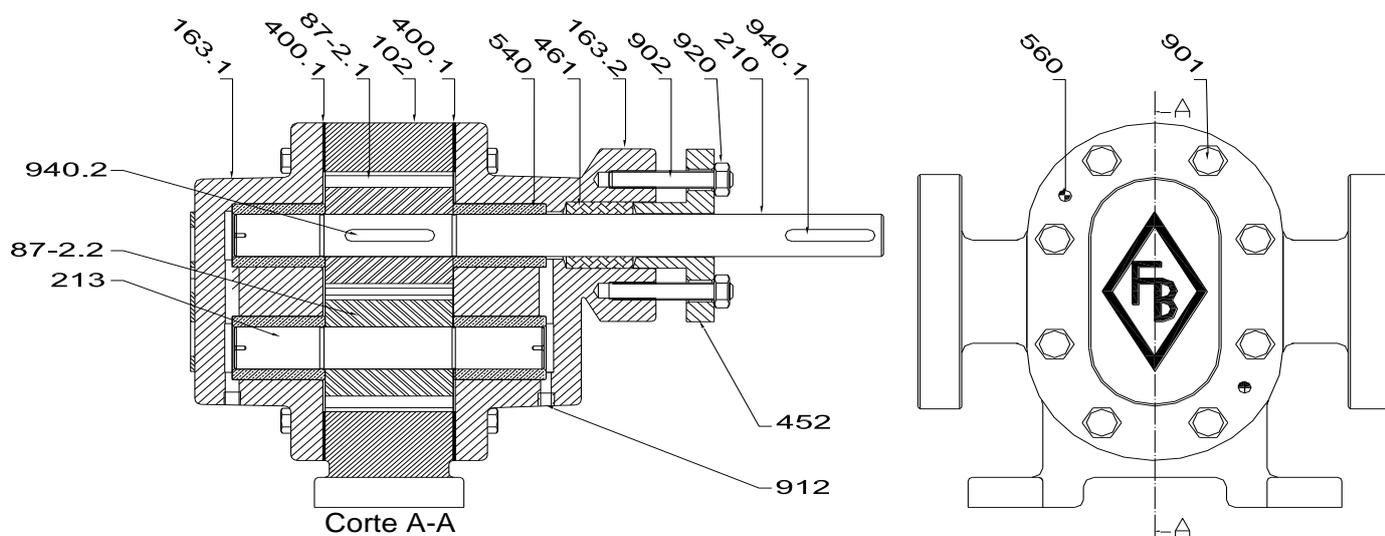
Desenho em Corte bomba FBE 1.1/2" – 2" – 3" com gaxeta
